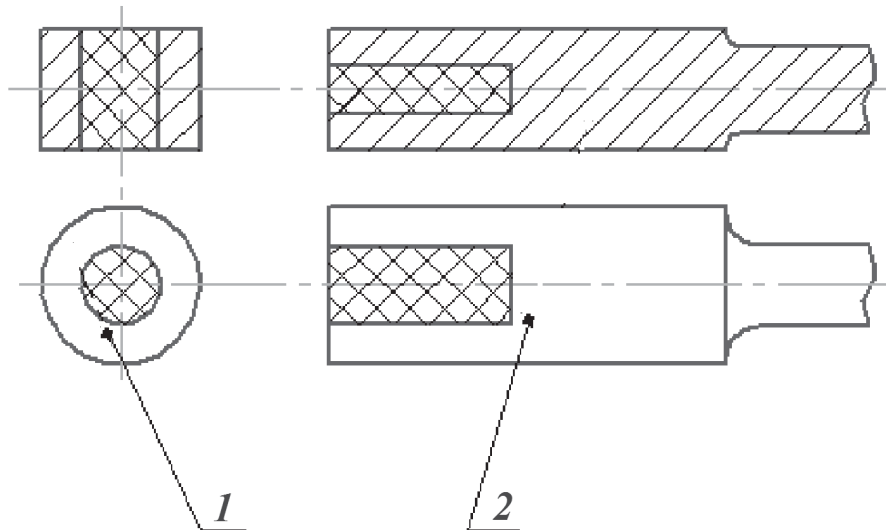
Схема расположения напусков для деталей типа втулки (1) и вилки (2)
